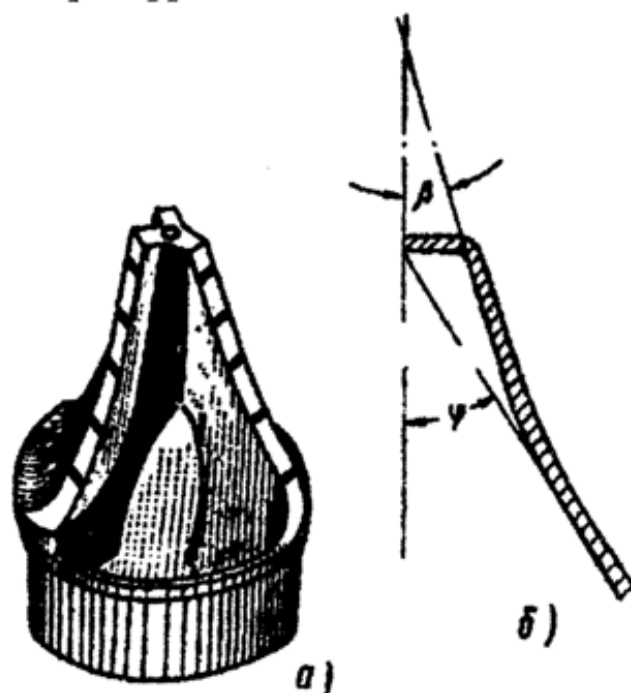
Черновая пальцевая фреза с уменьшенным числом зубьев:
